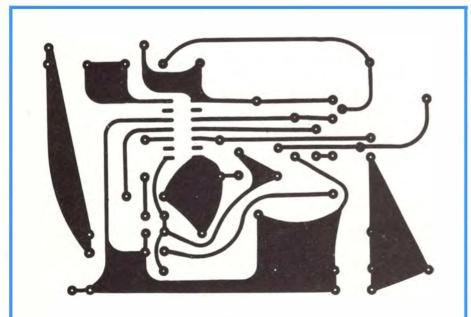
Disegno del circuito stampato dell'alimentatore duale in scala 1 : 1.
